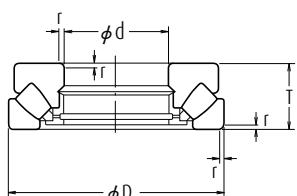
Rodamientos de Rodillos Esféricos de Empuje
